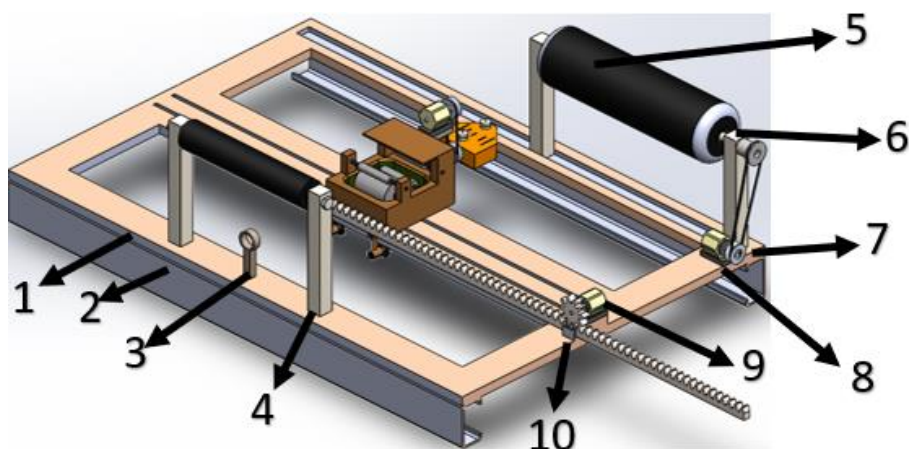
Diseño final máquina FILAMENT WINDING. Autor
